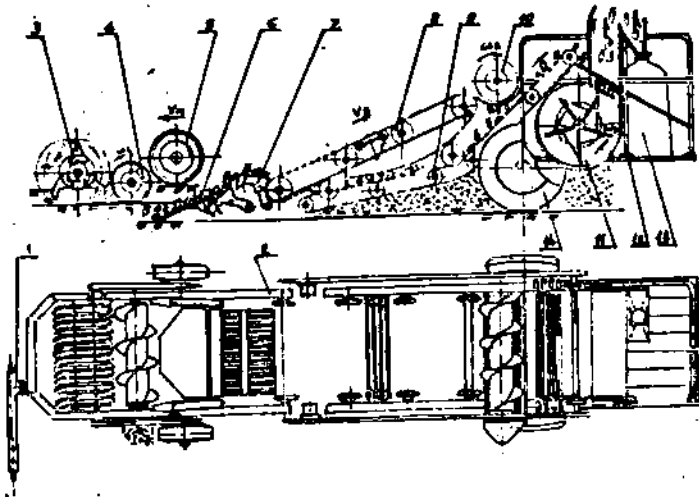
Схема машины: 1- прицепное устройство; 2- рама; 3- почвенная фреза; 4- шнек передний; 5- катки; 6- лемех; 7- стряхиватель кулачковый; 8- элеватор верхний; 9- элеватор нижний; 10- шнек задний; 11- решетка; 12- вентилятор; 13- площадка комбайнера; 14- колеса ходовые.
